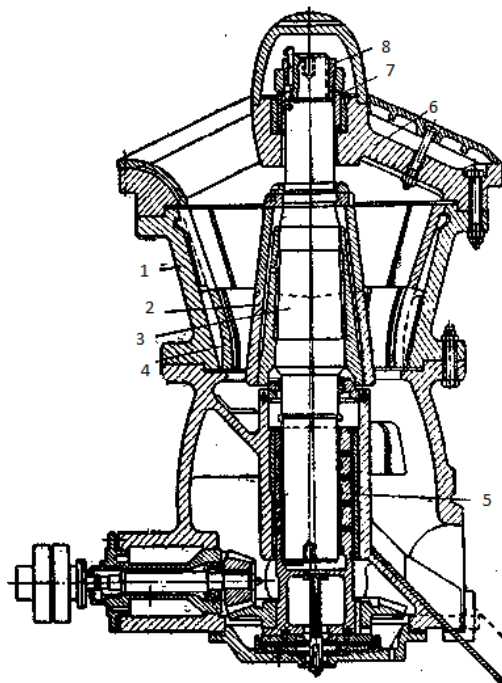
Конусна дробарка крупного здрібнення: 1 – корпус; 2 – дробильна головка; 3 – вертикальний (головний) вал; 4 – броньована плита; 5 – стакан-ексцентрик; 6 – хрестовина; 7 – конічна втулка; 8 – гайка.
